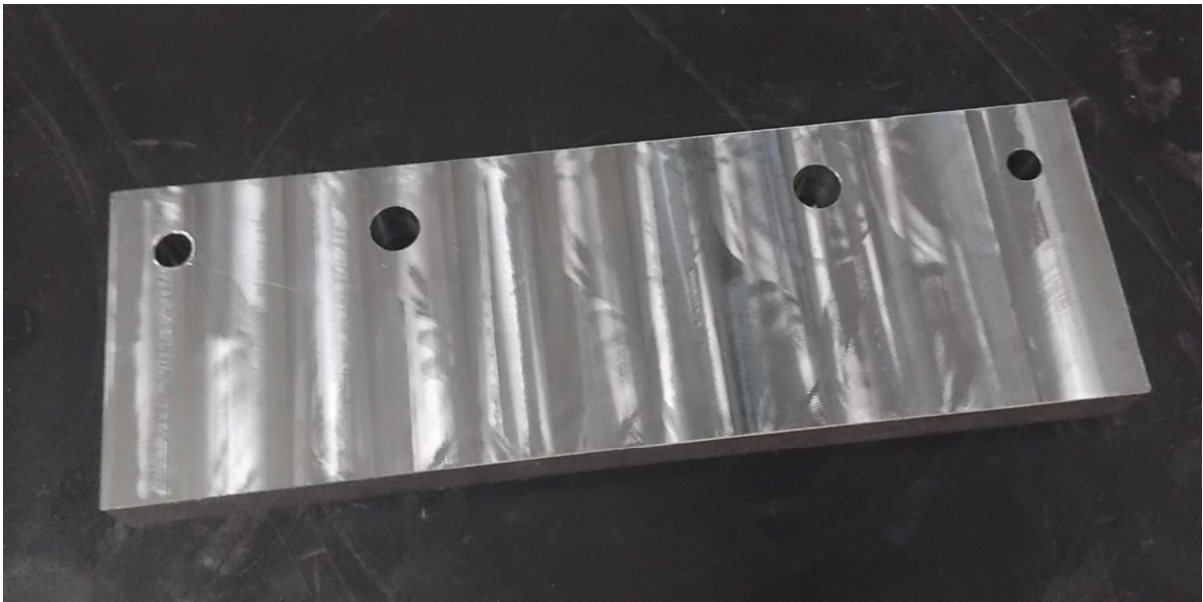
Image du montage d'usinage sur lequel se monte la pièce et où l'ensemble se monte sur l'équerre d'usinage
